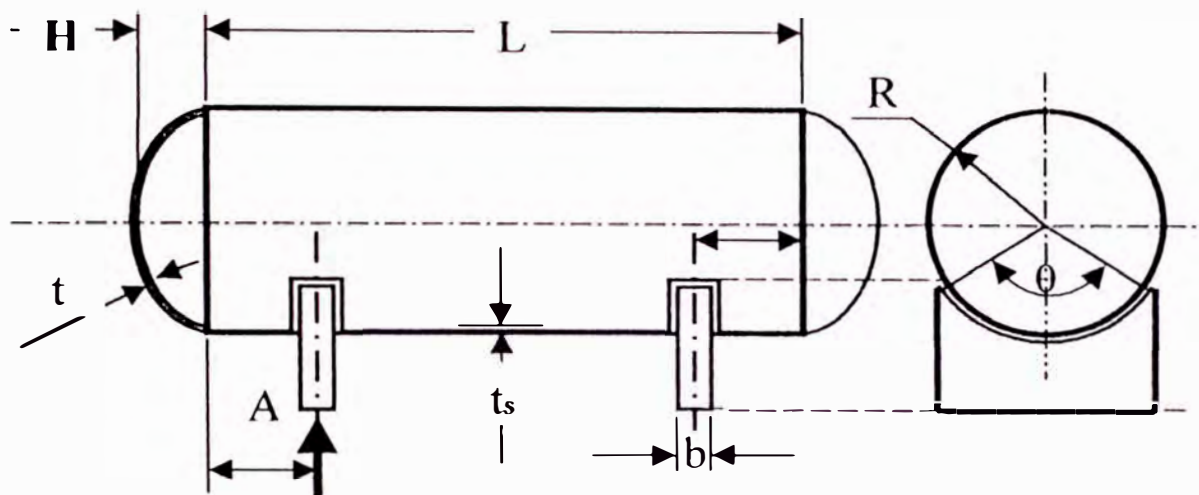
Parámetros estructurales principales para un separador horizontal
